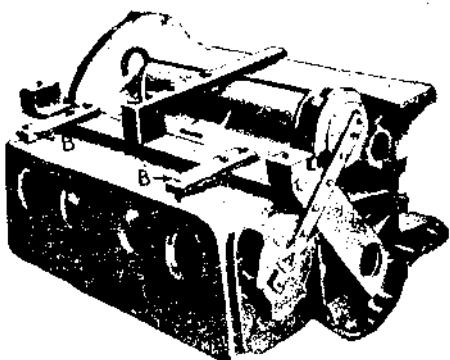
Приспособление для проверки отливки блока фирмы Yellow Sleeve Valve Co.
